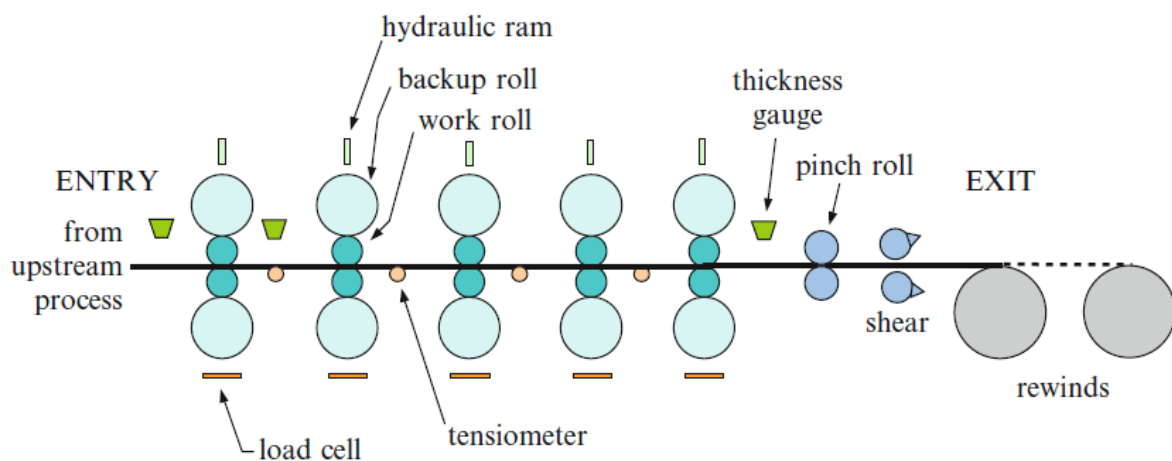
moulin froid tandem de Cinq-support, configuration continue
